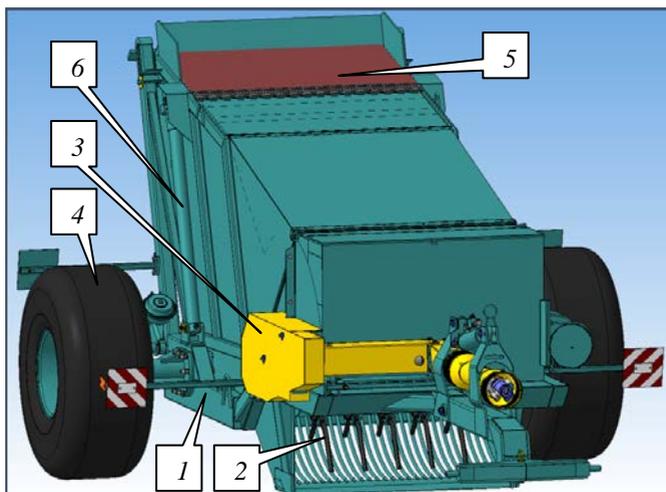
Схема подборщика ПВК-1,5: 1 – рама; 2 – барабан подъемный; 3 – трансмиссия; 4 – колеса опорные; 5 – бункер; 6 – гидроцилиндры опрокидывания бункера
